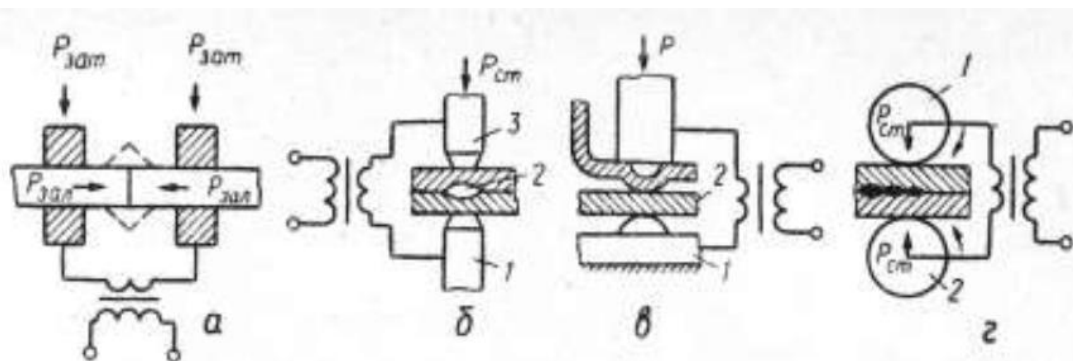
Схема контактної зварювання: а – стикового; б – точкового; в – рельєфного; г – шовного
